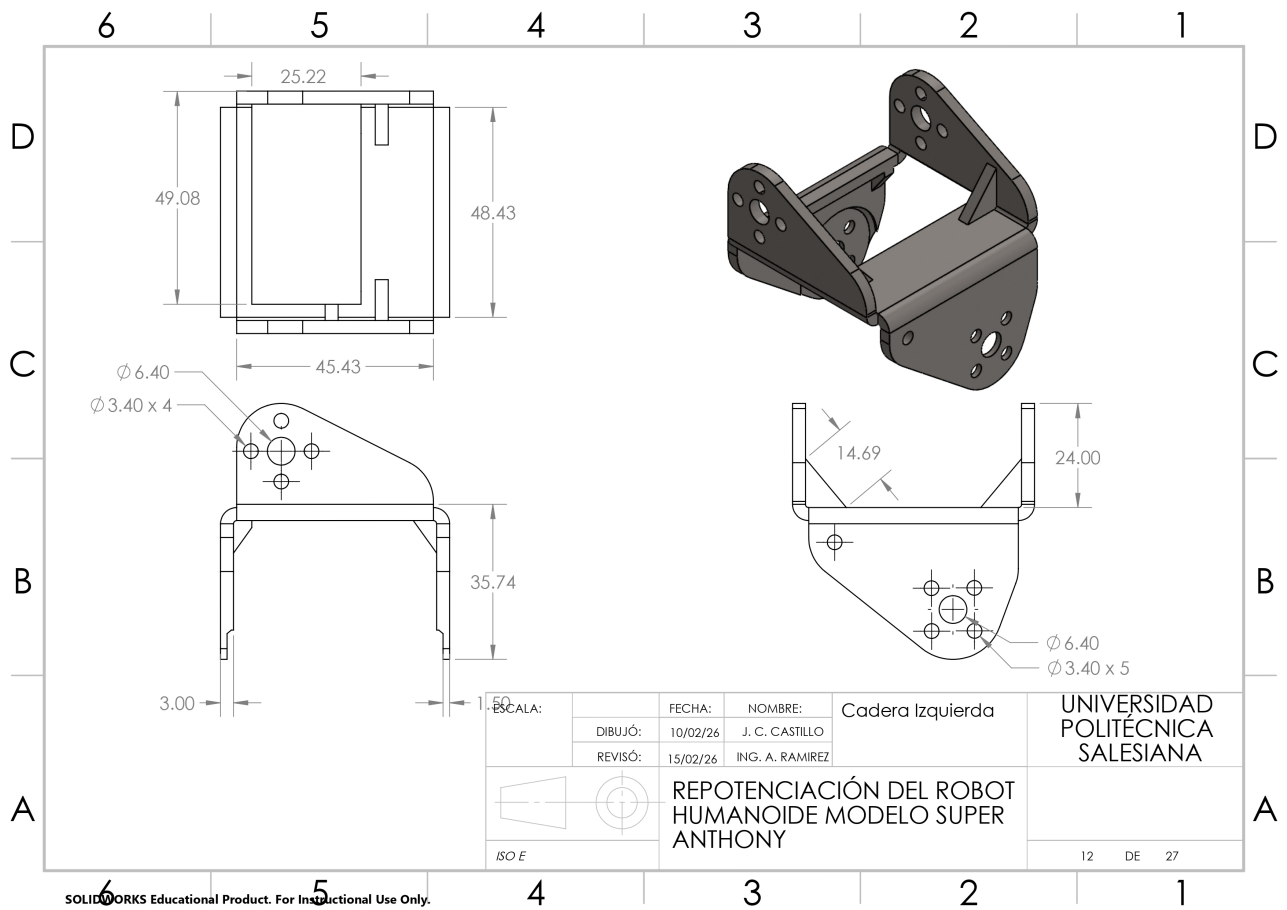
Lámina acotada de la cadera izquierda del robot humanoide, por J. Castillo y B. Gualle, Solidworks
